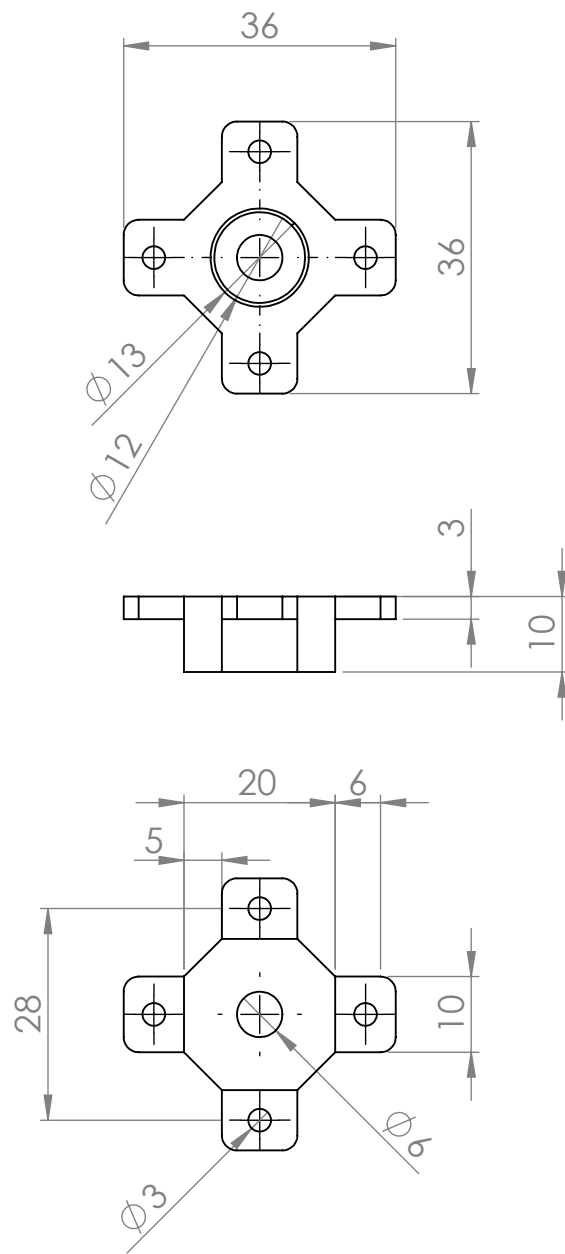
Diseño del molde para enmallado interno del *Robot Shear* parte B
